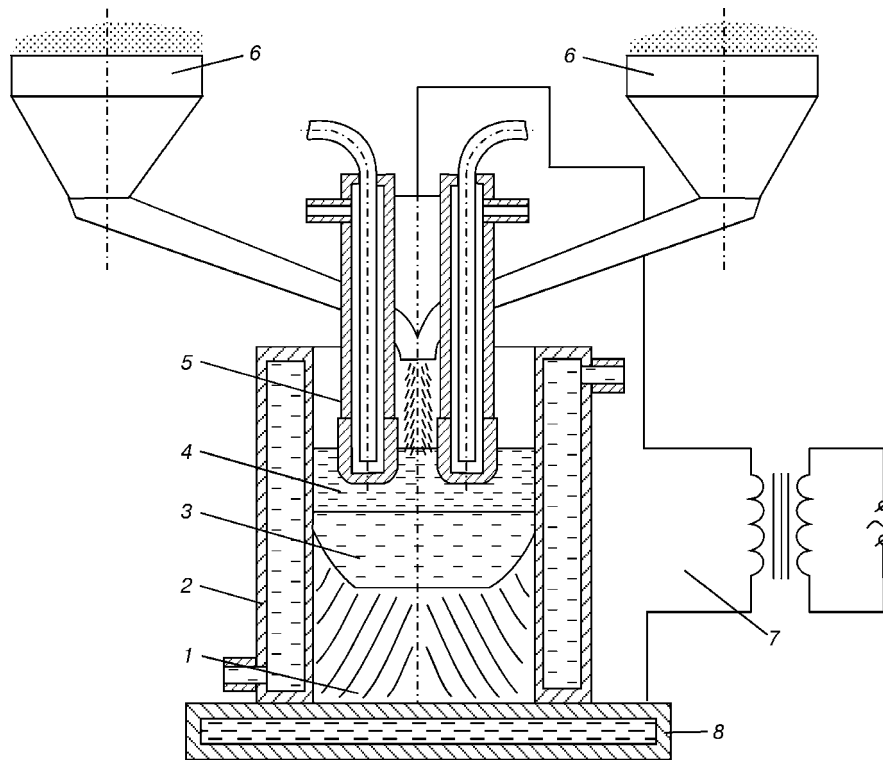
Схема процесса электрошлаковой выплавки ферротитана из титановой и стальной стружки: 1 — твердый металл; 2 — кристаллизатор; 3 — металлическая ванна; 4 — шлаковая ванна; 5 — нерасходуемый электрод; 6 — бункера со стальной и титановой стружкой; 7 — источник питания; 8 — поддон
